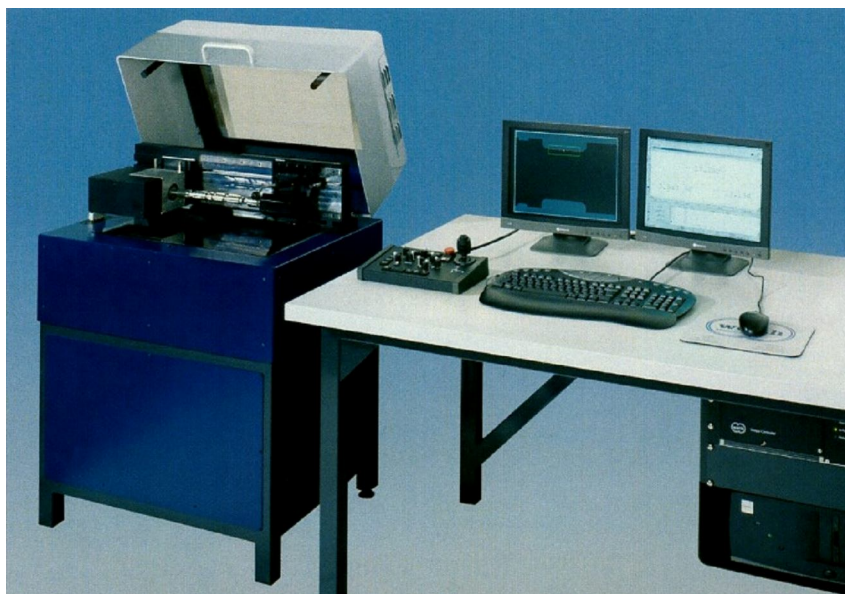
Измерительный проектор Shaft Score, «Werth Messtechnik GmbH»
